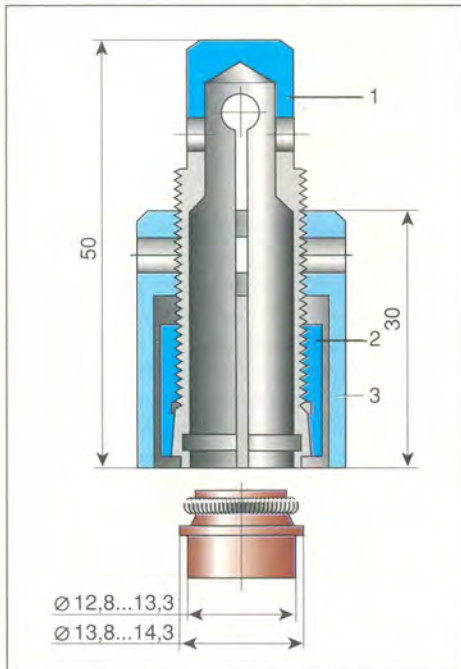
Цанговое приспособление для снятия маслоотражательных колпачков ("Жигули", "Нива"): 1-цанга; 2-гайка цанги; 3-гайка упорная
